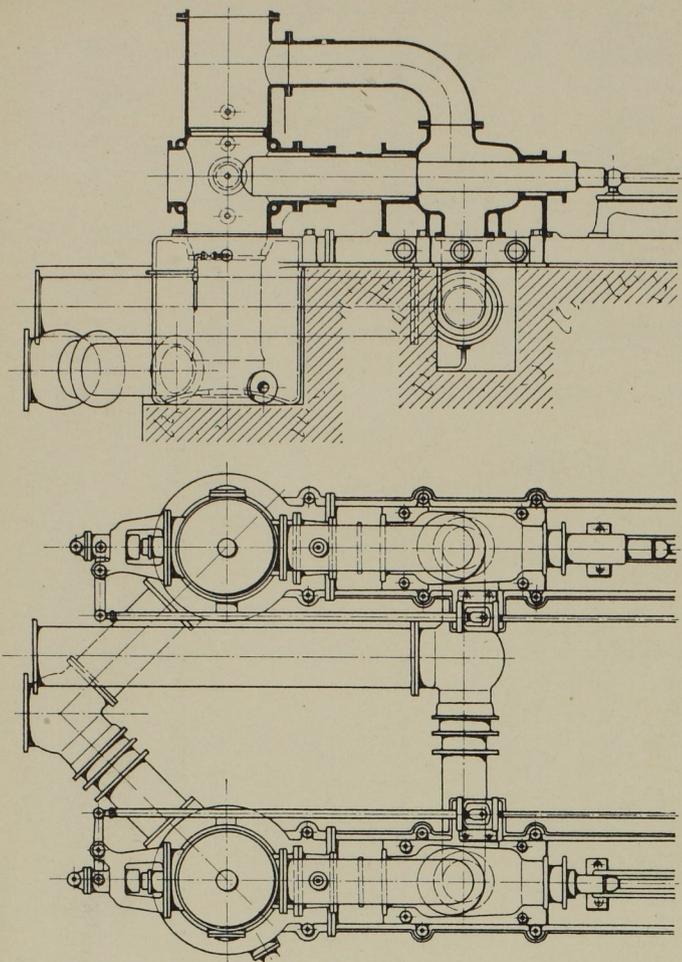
Längsschnitt und Grundriss der Pumpe. Masst. 1:50.
